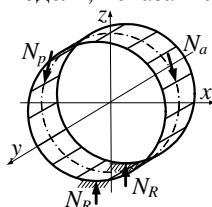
Схема нагружения полимерного сепаратора усовершенствованной конструкции
